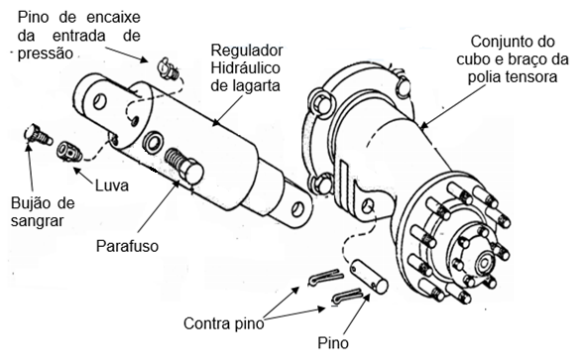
COMPONENTES DO REGULADOR HIDRÁULICO
